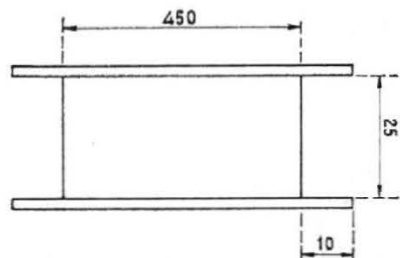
Carcasse destinée à la fabrication d'une bobine pour la désaimantation des pièces en métal magnétique du tube ou des pièces environnantes
